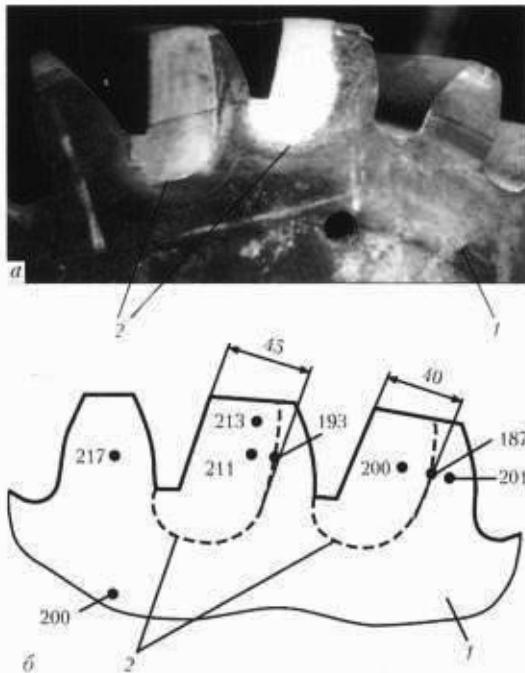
Внешний вид торцевых частей зубьев после ЭШН и механической обработки прибыльных участков (а) и схема формы и глубины провара зубьев (б): 1 — торец вал-шестерни; 2 — форма провара; точками указаны места и значения твердости по HB
